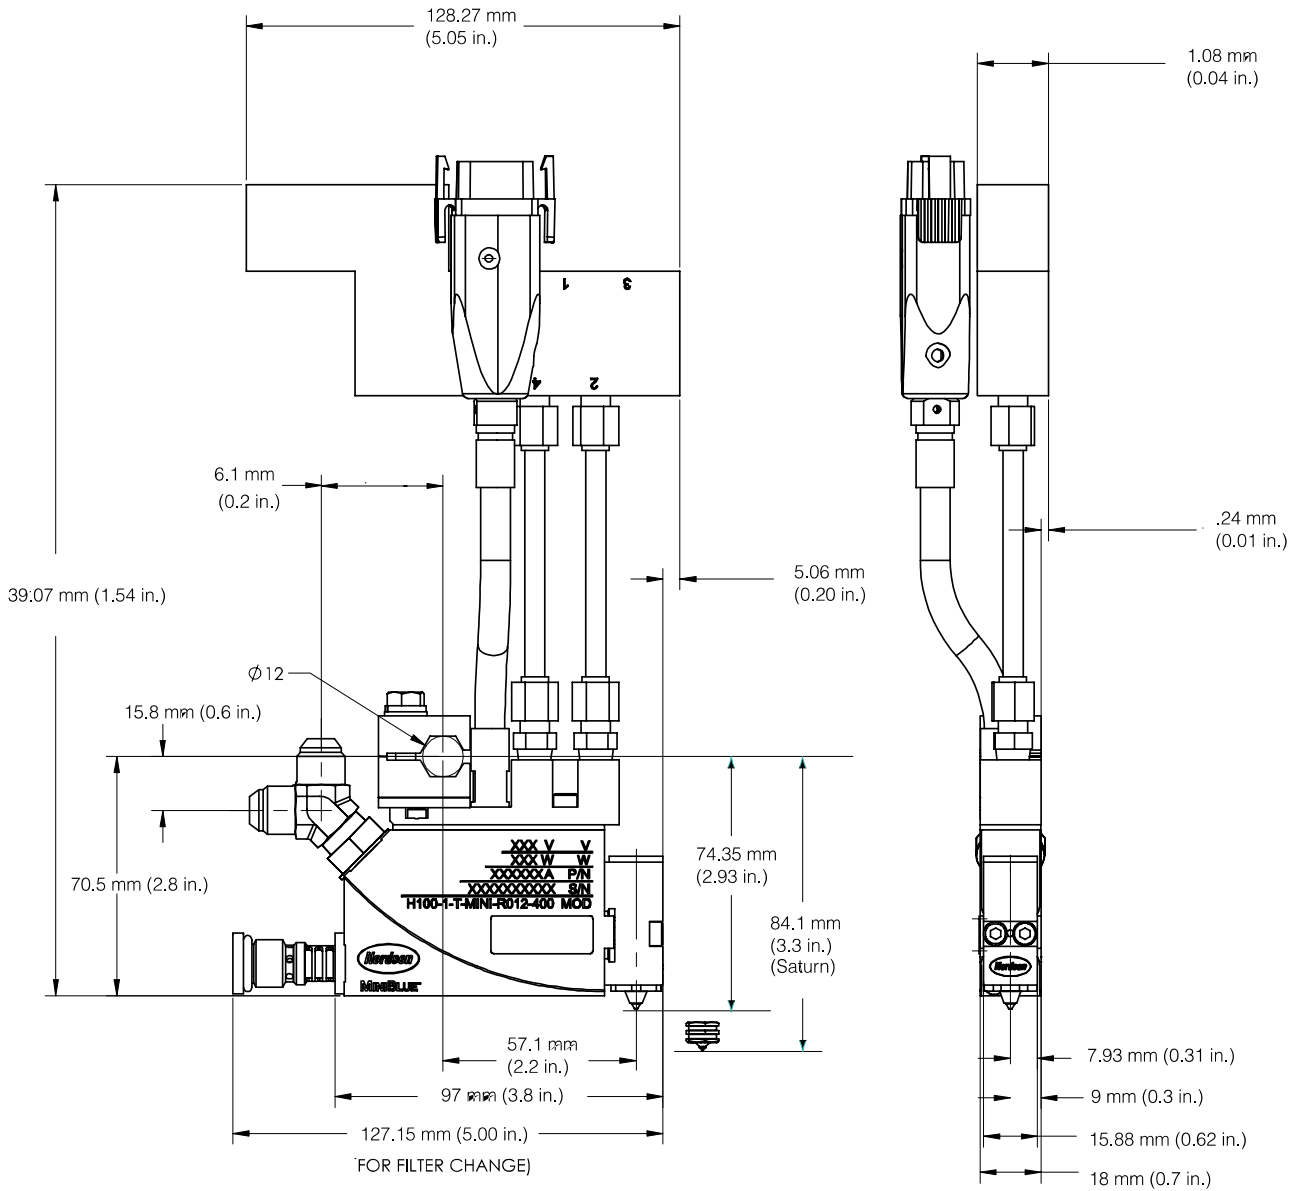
Dimensiones de una pistola delgada de un módulo con una electroválvula SG
